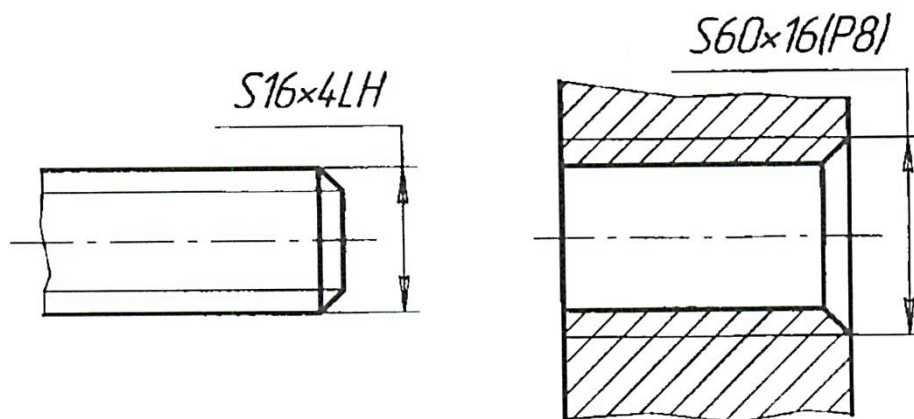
Обозначение резьбы упорной на чертежах
